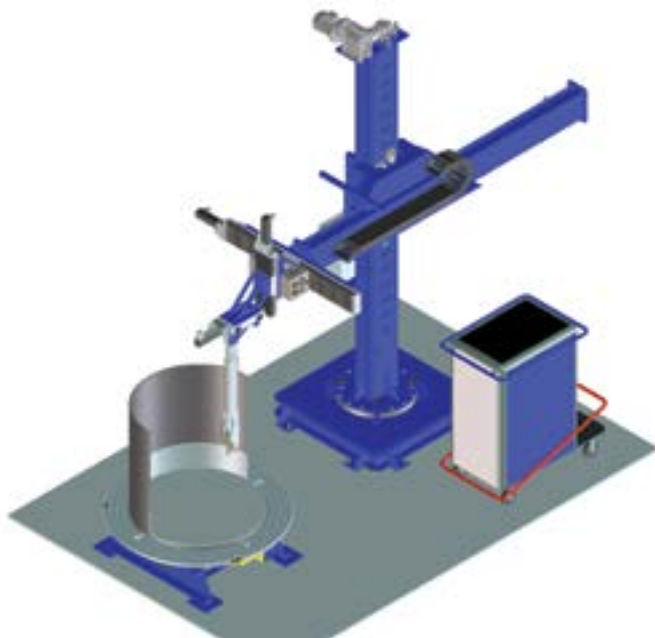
Схема установки для наплавки горизонтальных швов на вертикальной поверхности вращающейся детали
